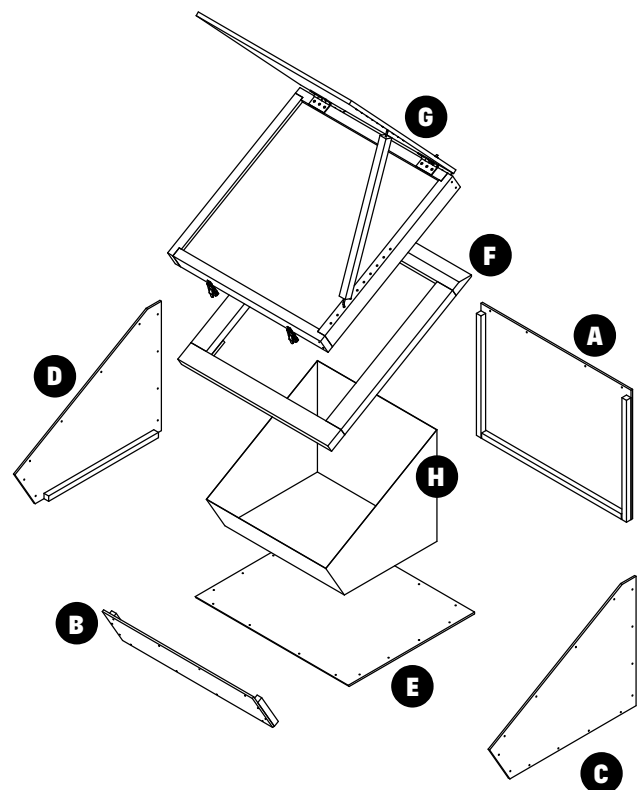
Vue éclatée et numérotation des sous-ensembles
